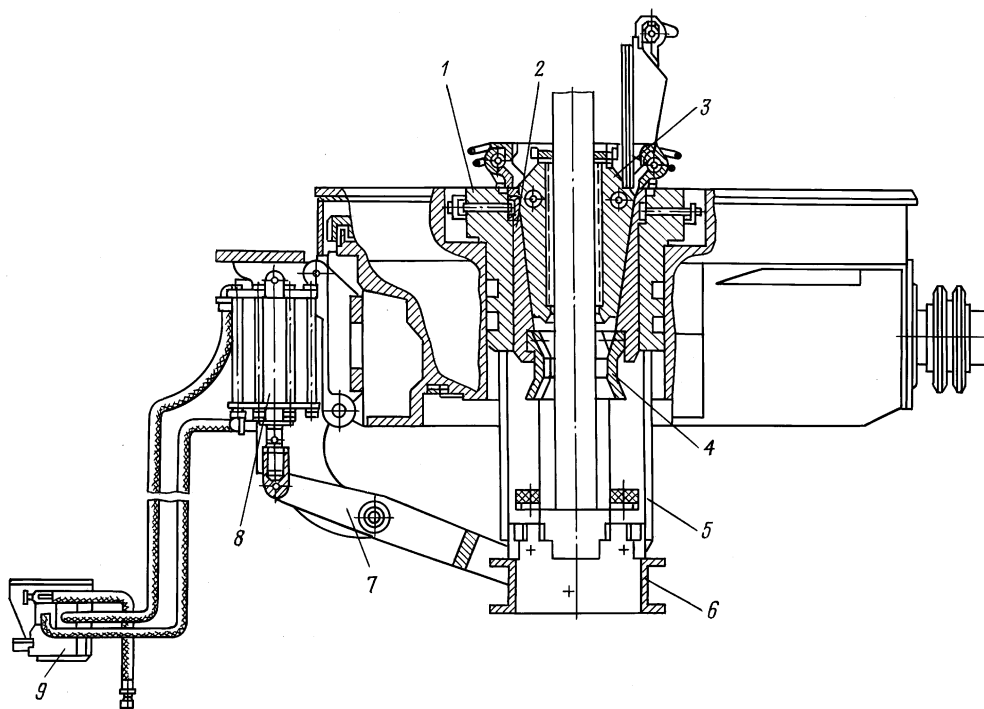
Клиновой пневматический захват ПКР560М:
